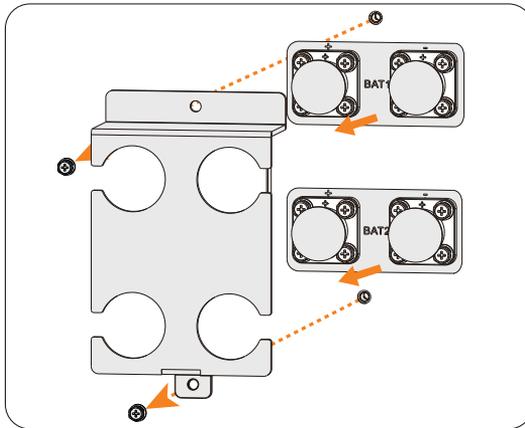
Die Schutzabdeckung der Batterie entfernen
